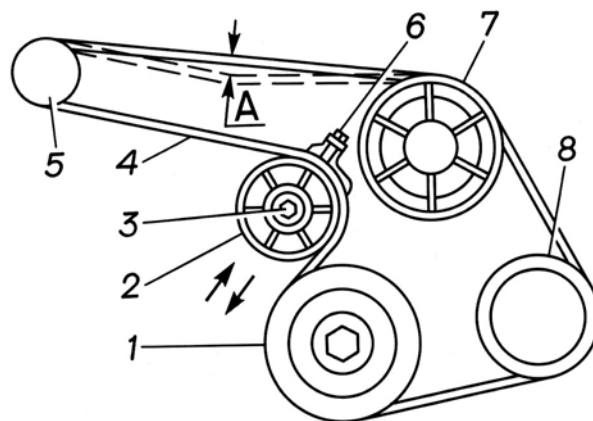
Схема натяжения ремня привода агрегатов: $A=14$ мм; 1 - шкив коленчатого вала; 2 - натяжной ролик; 3 - болт крепления натяжного ролика; 4 - поликлиновой ремень; 5 - шкив генератора; 6 - болт перемещения натяжного ролика; 7 - шкив водяного насоса; 8 - шкив насоса ГУР
